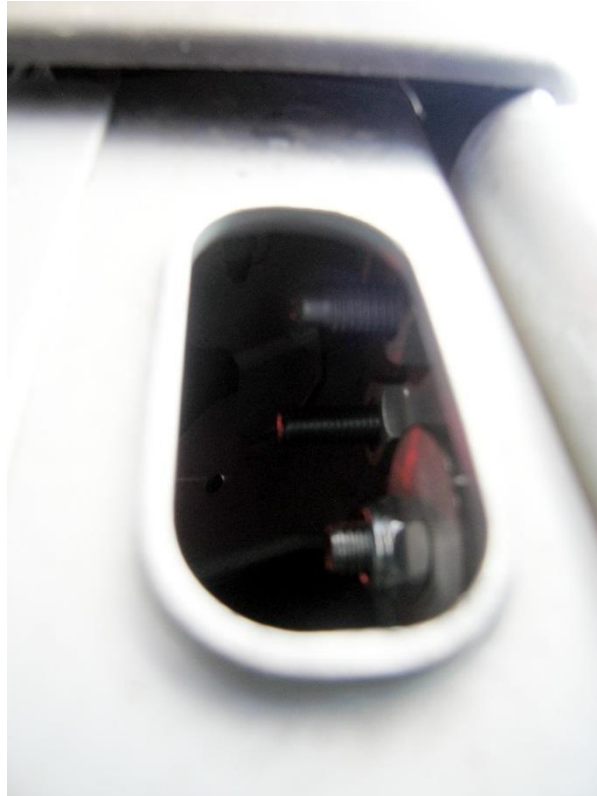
Blick auf die obere Einpressmutter mit durchragender Sechskantschraube
